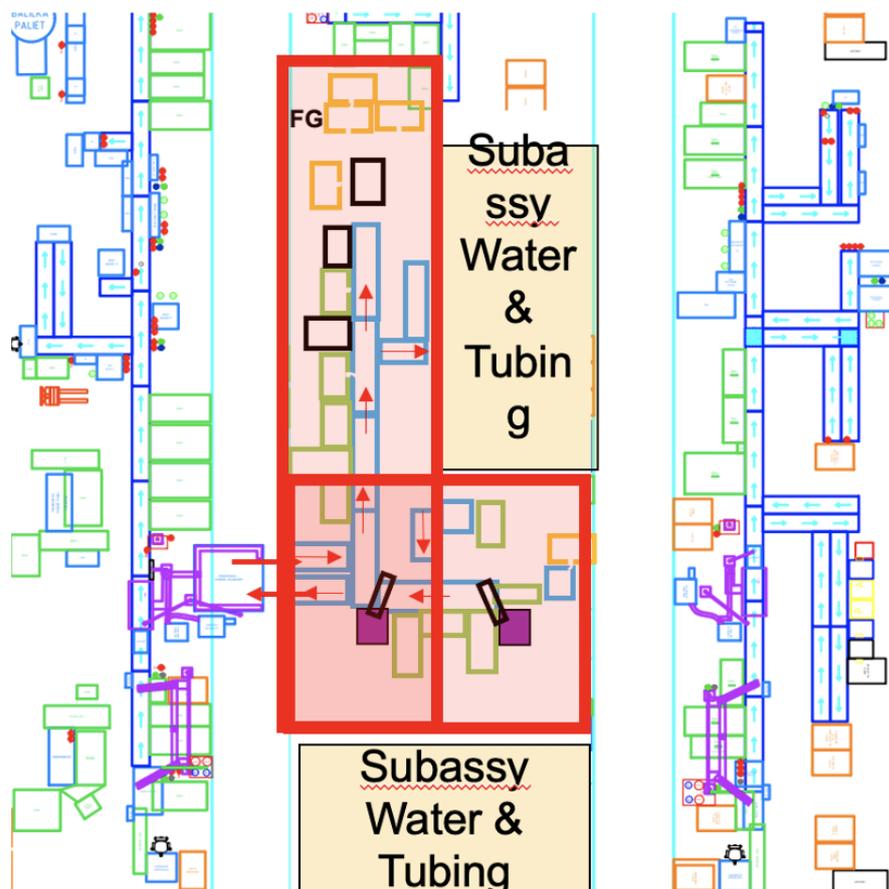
Varianta layoutu A (vlastné spracovanie)
